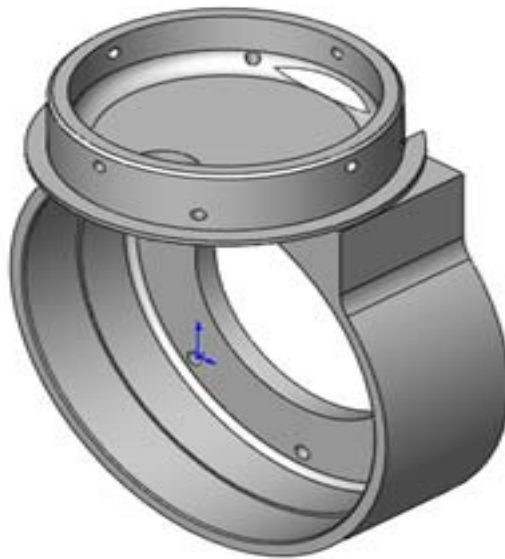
Vista 3-D de pieza de giro a tubo.
